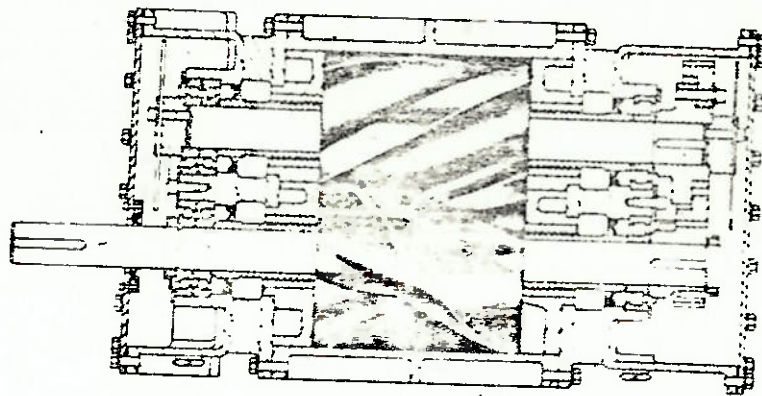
soprador de deslocamento positivo com rotor lobulado espiralmente
